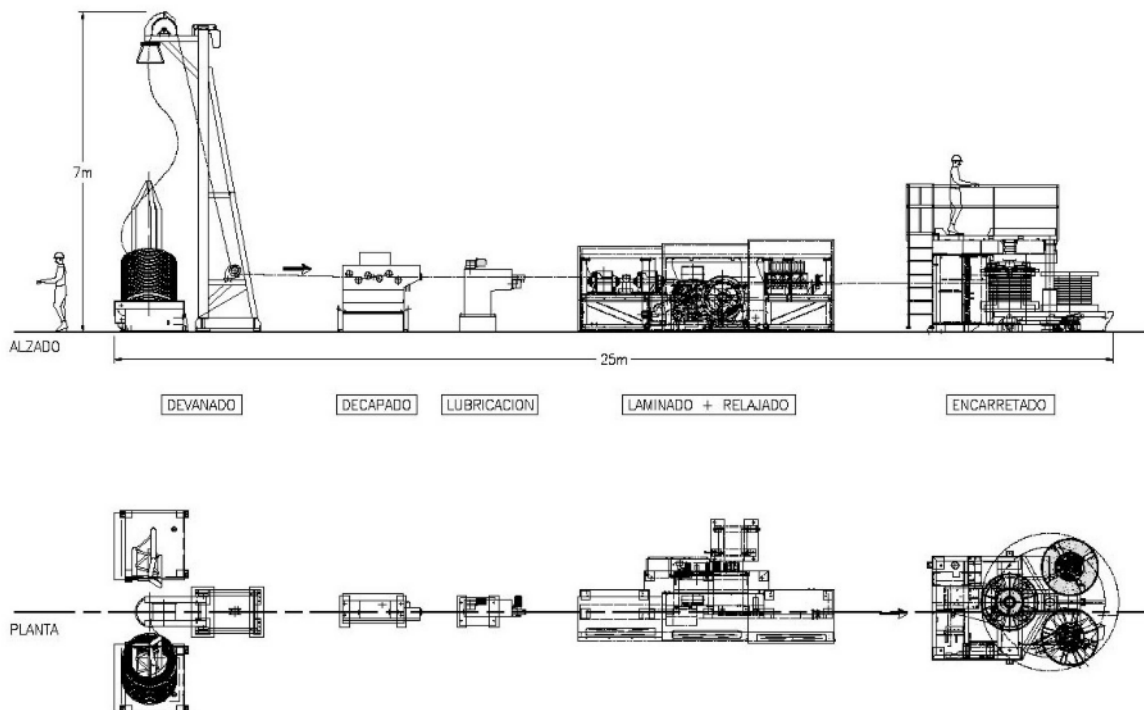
Dibujo de una máquina actual de laminado en frío de armaduras.
